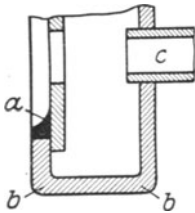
Unterer Teil einer neueren Ausführung der Wasserkammer. Die älteren Wasserkammern haben bei b Schweißstellen, die schwierig auszuführen waren und durch Aufreißen zu Kesselexplosionen Anlaß gaben. Die Schweißstelle a der neueren Wasserkammern ist sicherer herzustellen, c = die unterste Reihe der Siederohre.
